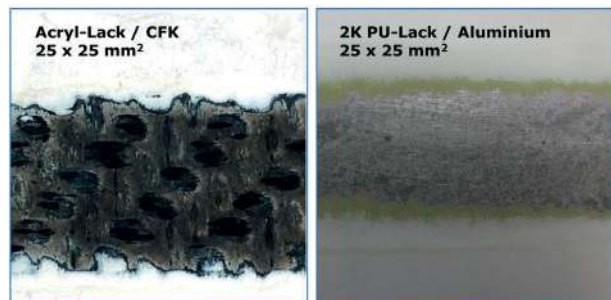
Vergleich der Schichtabtragung von einem Kohlefaserbauteil und einem Aluminiumbauteil. Deutlich zu sehen ist, dass bei dem CFK Bauteil die Faser freigelegt, aber nicht geschädigt wird. Beim dem Aluminiumträger wird die ursprüngliche Oberflächenbearbeitung (Schleifspuren) sichtbar
